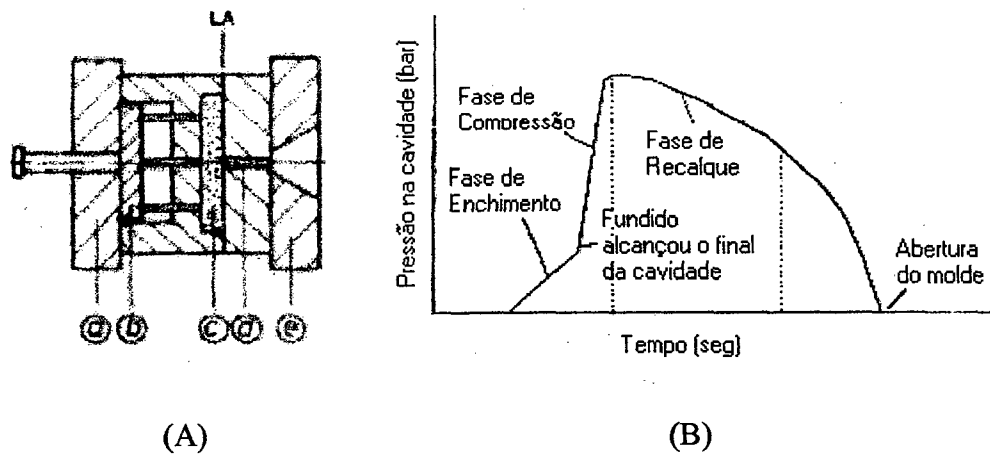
Molde para injeção: (A) Partes principais: a) placa móvel; b) sistema de extração; c) cavidade; d) canal de alimentação; e) placa fixa; LA: linha de abertura do molde.
